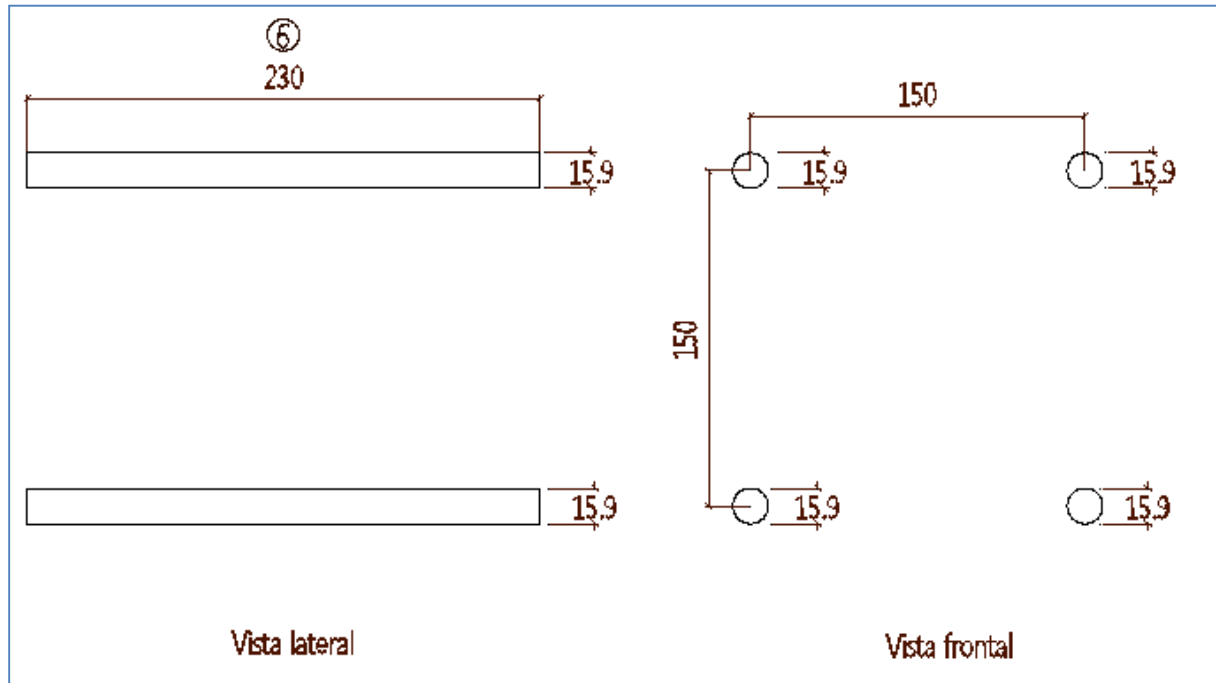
Detalle despiece pieza No.6 modelo 2 tensión.
